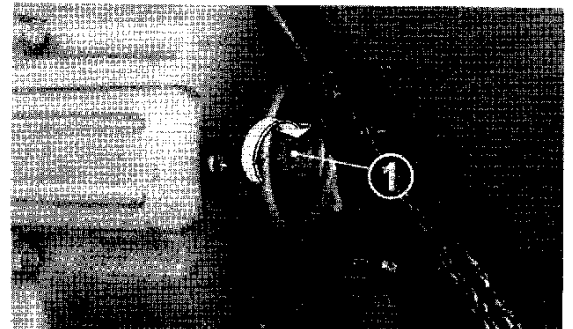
(1) Lichtmaschinenrotor-Befestigungsschraube
